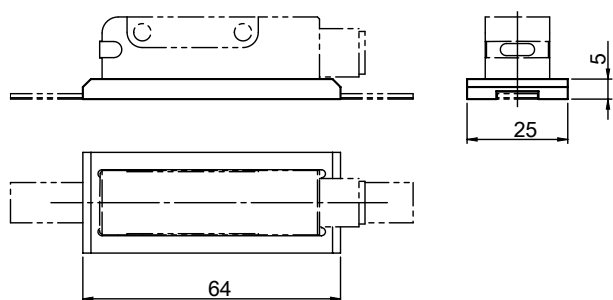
Guía de sensor BAM TO-ML-019-SL1
